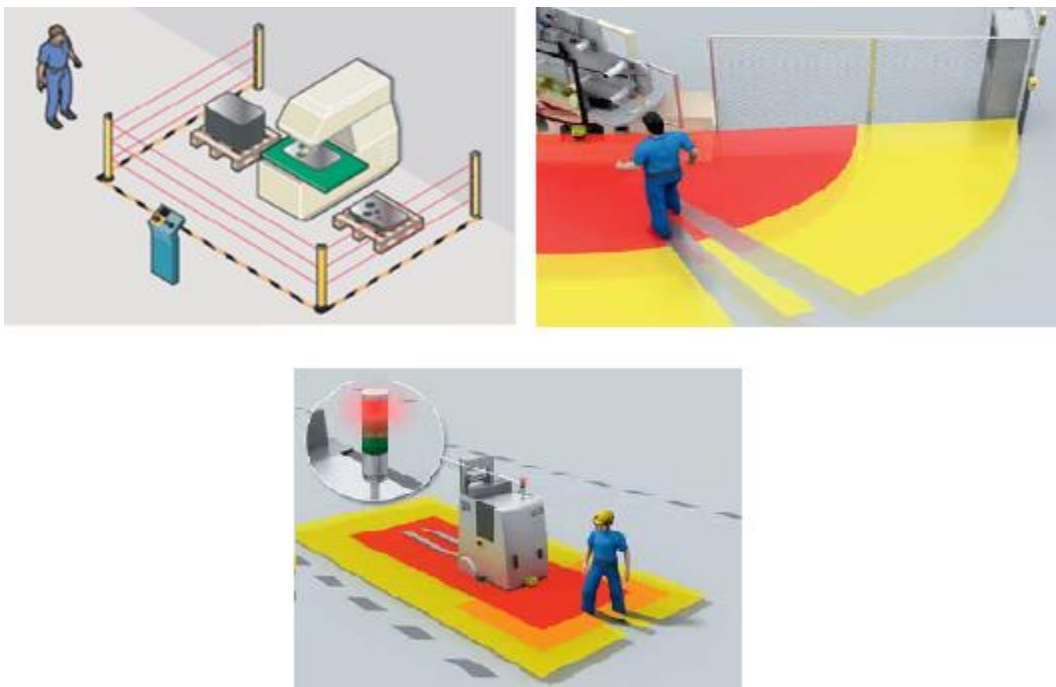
Barreiras ou cortinas para detecção de intrusos (Sick, 2014)
